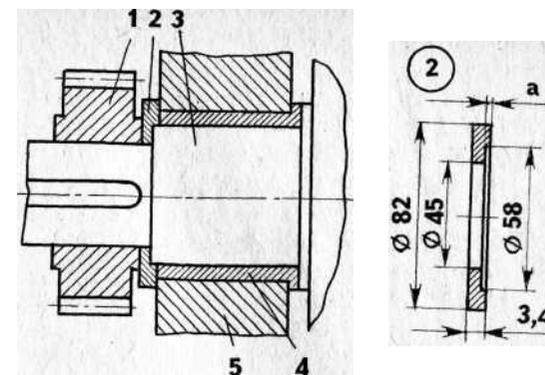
Узел передней опоры коленчатого вала: 1 — шестерня газораспределительного механизма; 2 — шайба; 3 — коленчатый вал; 4 — подшипник; 5 — опора подшипника. Размер "а" зависит от величины, на которую изношен буртик подшипника.
